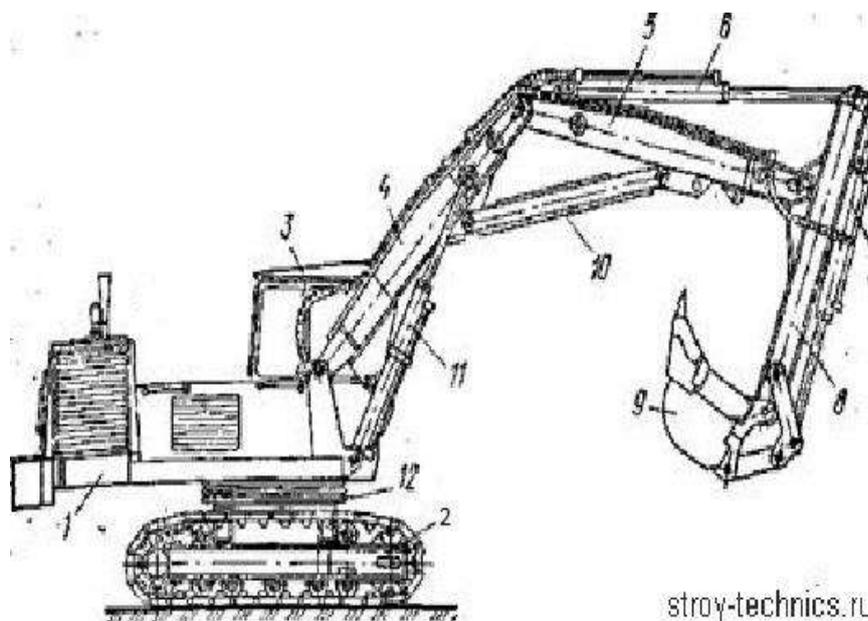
Экскаватор универсальный с жесткой подвеской рабочего оборудования: 1 - поворотная платформа; 2 - гусеничное ходовое устройство; 3 - кабина машиниста; 4 - стрела; 5 - удлинитель стрелы; 6 - гидроцилиндр подъема стрелы; 7 - гидроцилиндр поворота рукояти; 8 - рукоять; 9 - ковши; 10 - соединительная тяга; 11 - гидроцилиндр поворота ковша; 12 - роликовый опорно-поворотный круг.
